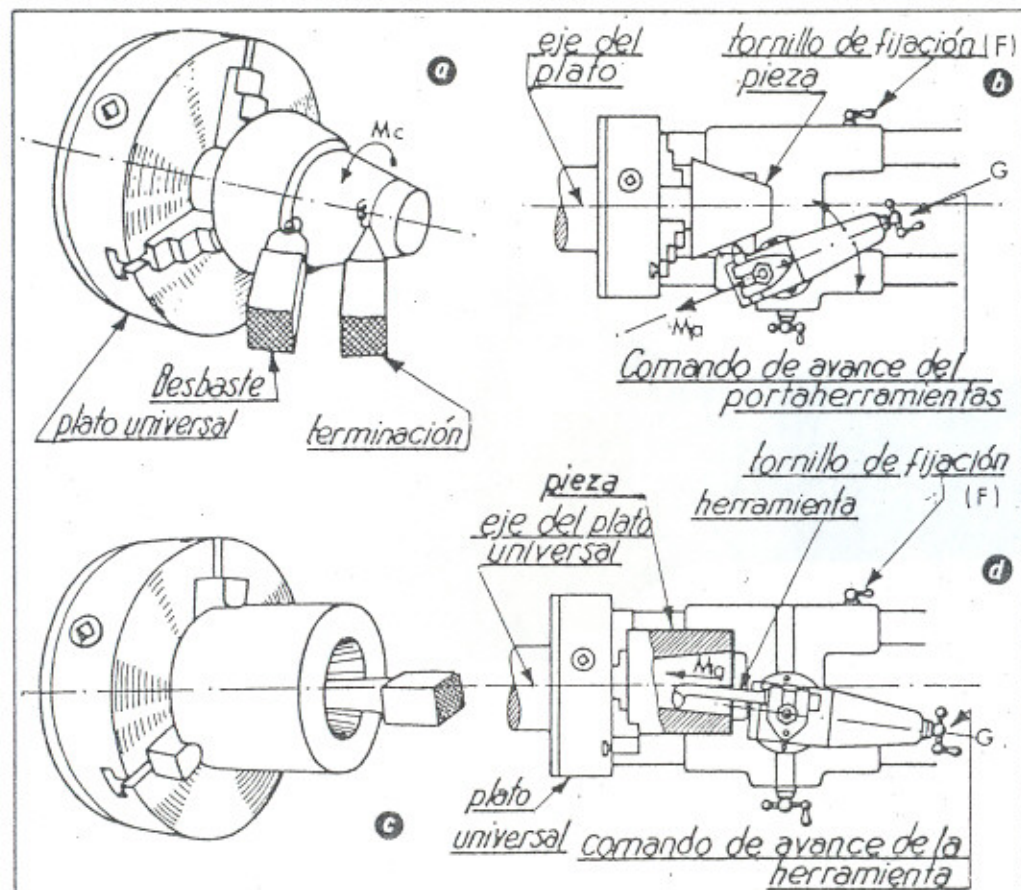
a) Proceso de torneado de conos cortos montados "al vuelo". b) Comando de avance del porta-herramientas. c) Proceso de torneado interior, de conos cortos, "al vuelo". d) Comando de avance del porta-herramientas.
